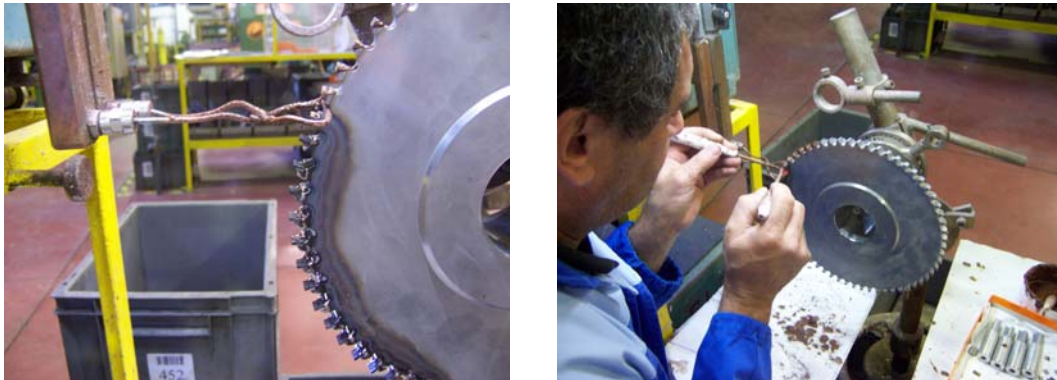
Aspecto das ferramentas após operação de fresagem:
